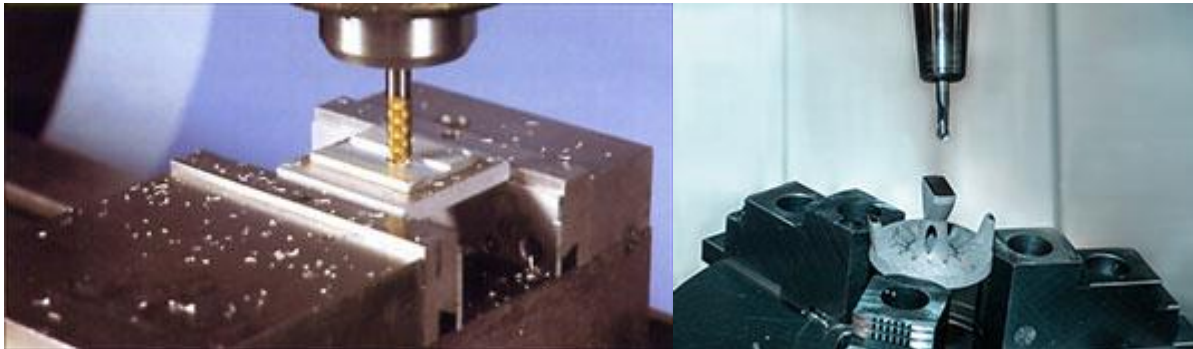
Geklebtes Werkstück auf Aluminiumgrundplatte und additiv gefertigtes Bauteil gehalten in einem Dreiflankenfutter (Quelle: Spanntech, Freyer Feinmechanik)
